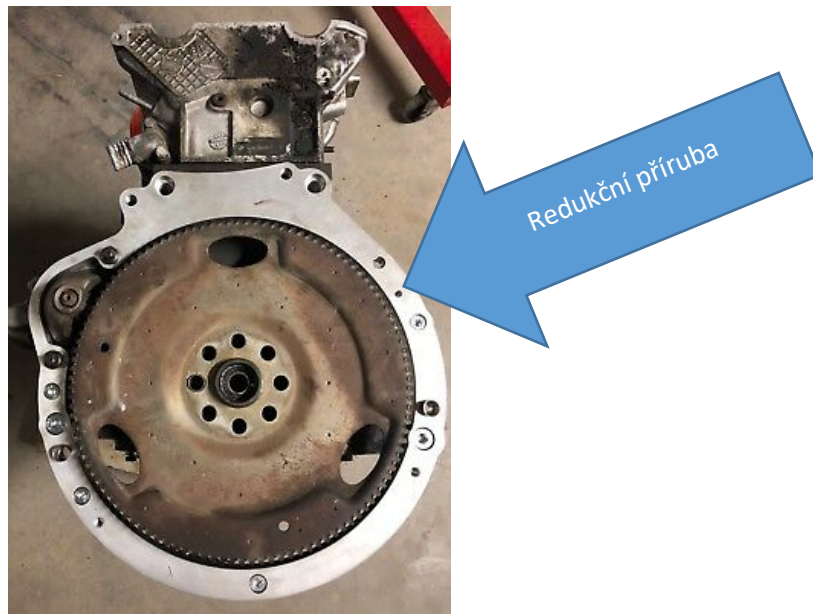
Šroubový spoj připravený na spojení s hliníkovým držákem motoru
